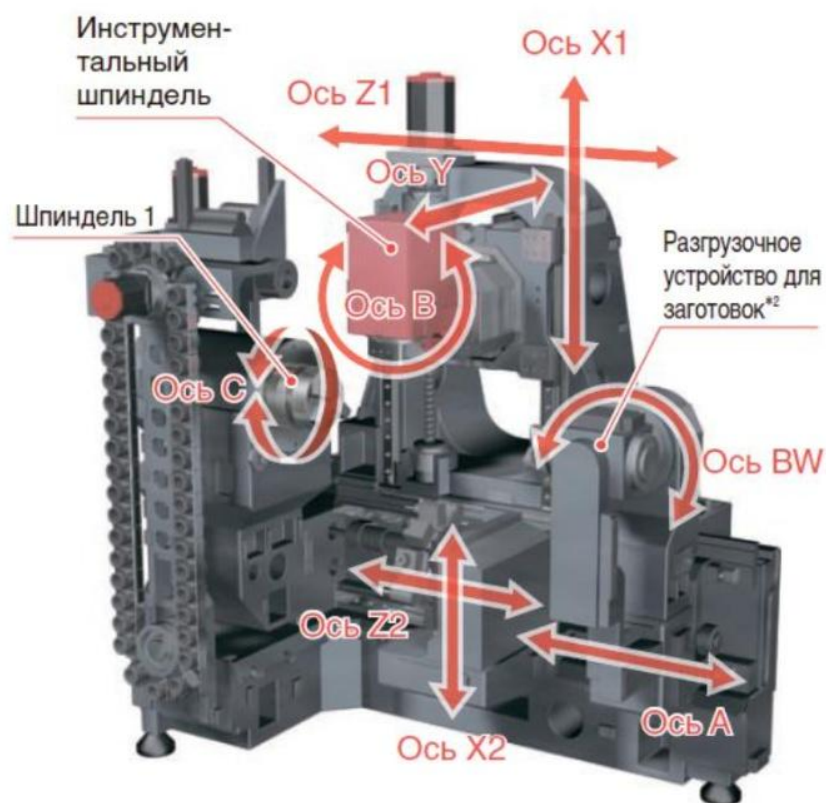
Модель рабочей зоны станка NTX 1000
